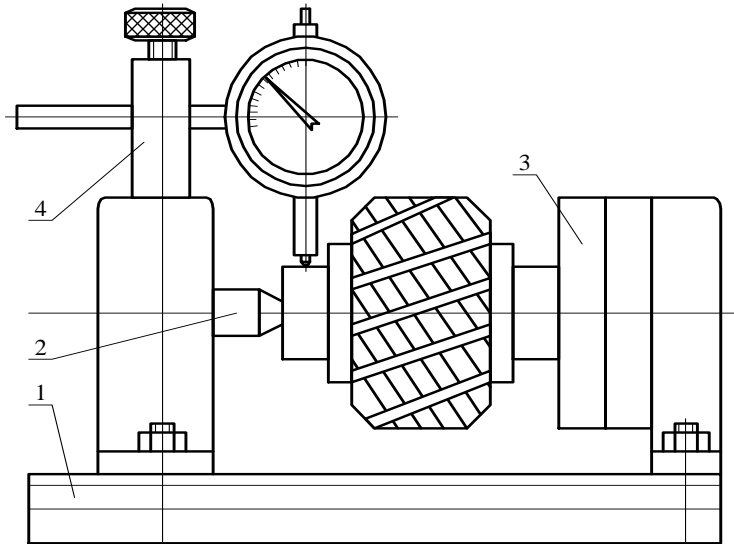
Пристрій для контролю черв'ячної фрези:
